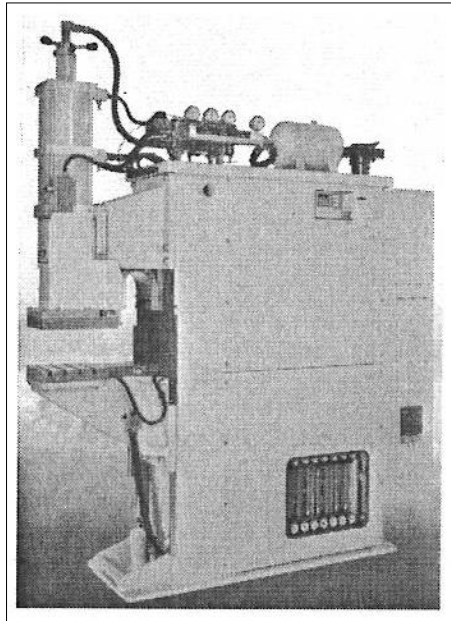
Prensa apta para procesos de soldadura por proyección.
